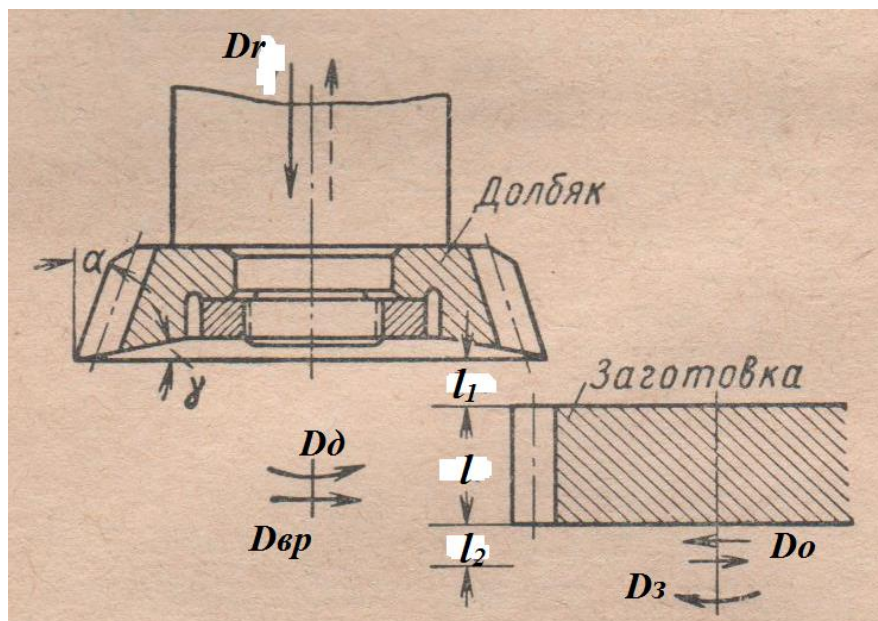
Схема нарезание зубчатых колёс долбьяками
